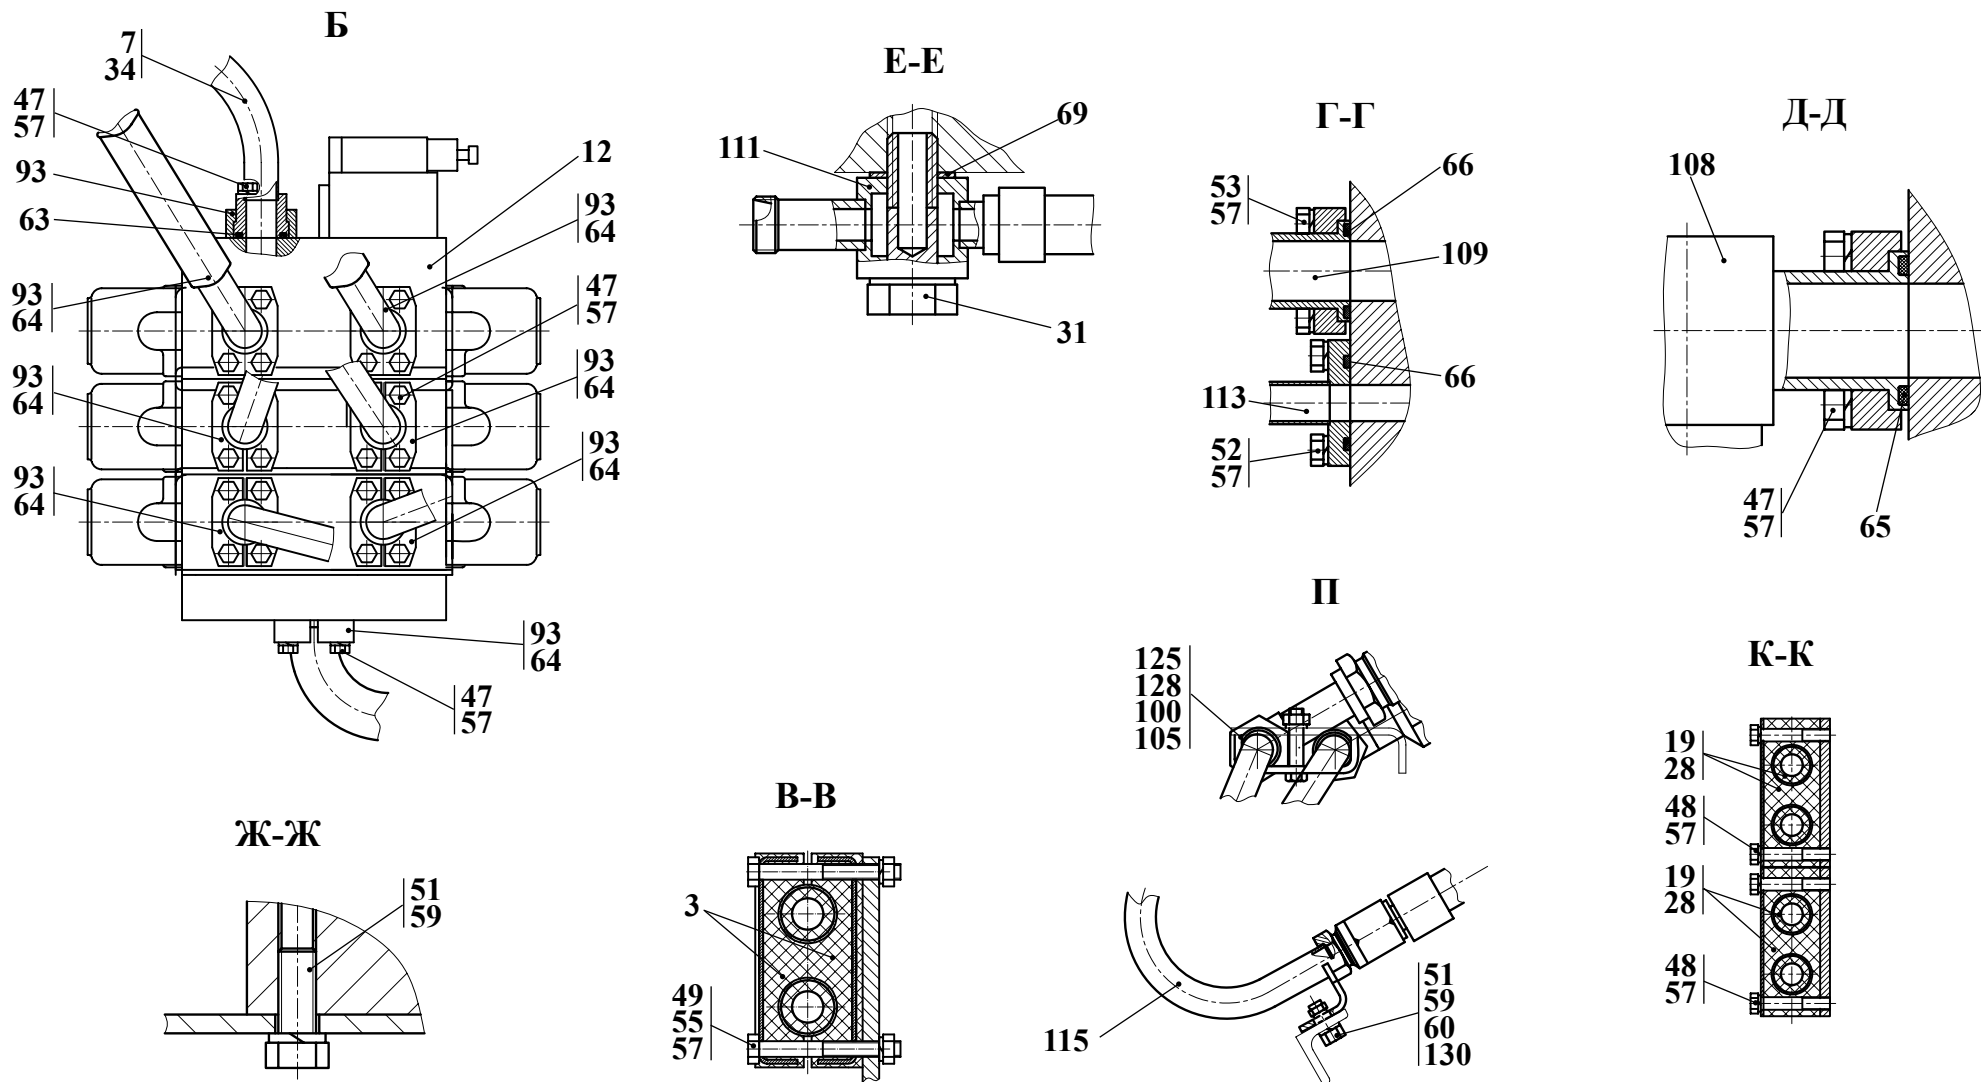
342P.36.00.000-Б	Гидросистема погрузочного оборудования
